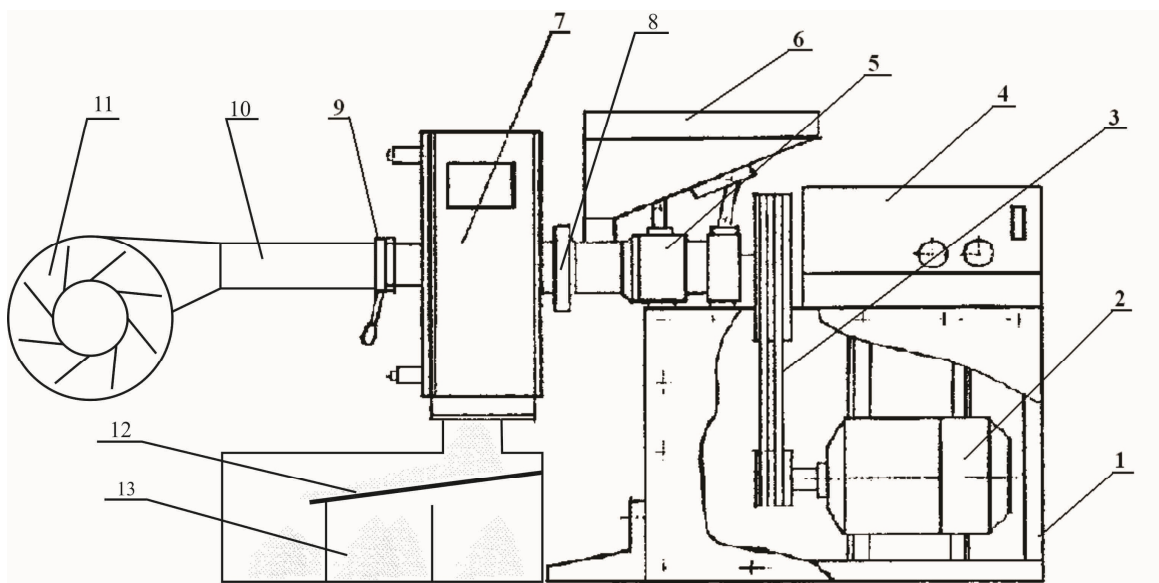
Кинематическая схема универсального станка ММП 150/50
